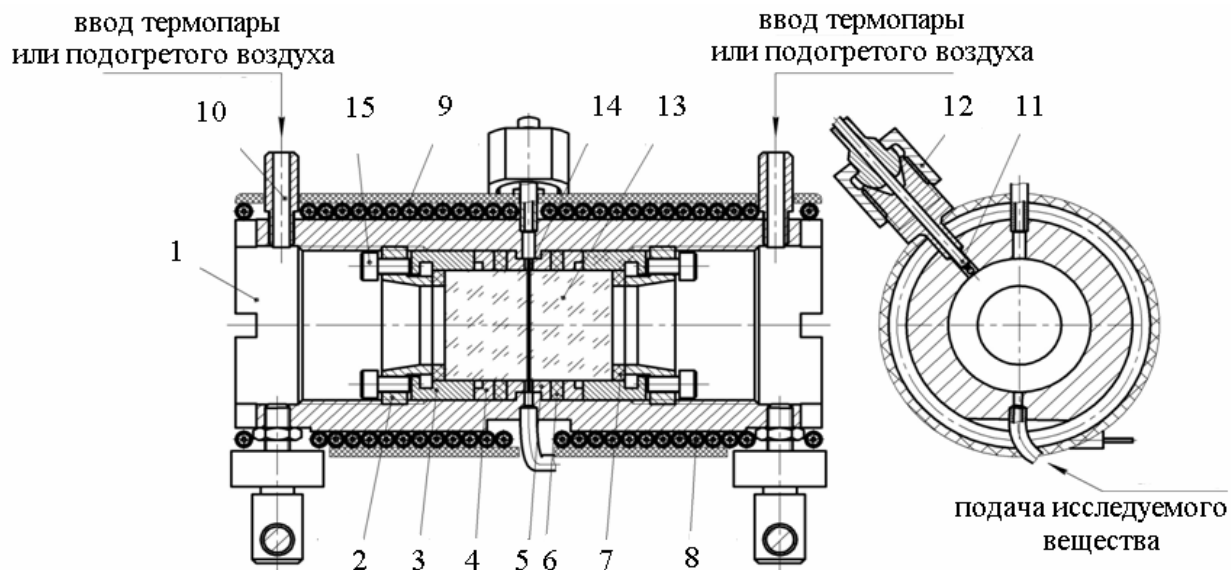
Измерительная ячейка: 1 - корпус; 2 - гайка; 3 - втулка; 4, 5 - кольцо; 6 - уплотнитель; 7 - прокладка; 8 - нагреватель; 9 - изоляция; 10 - оливка; 11 - термомпара; 12 - гайка; 13 - кристаллы; 14 - разрезное кольцо; 15 - винт
